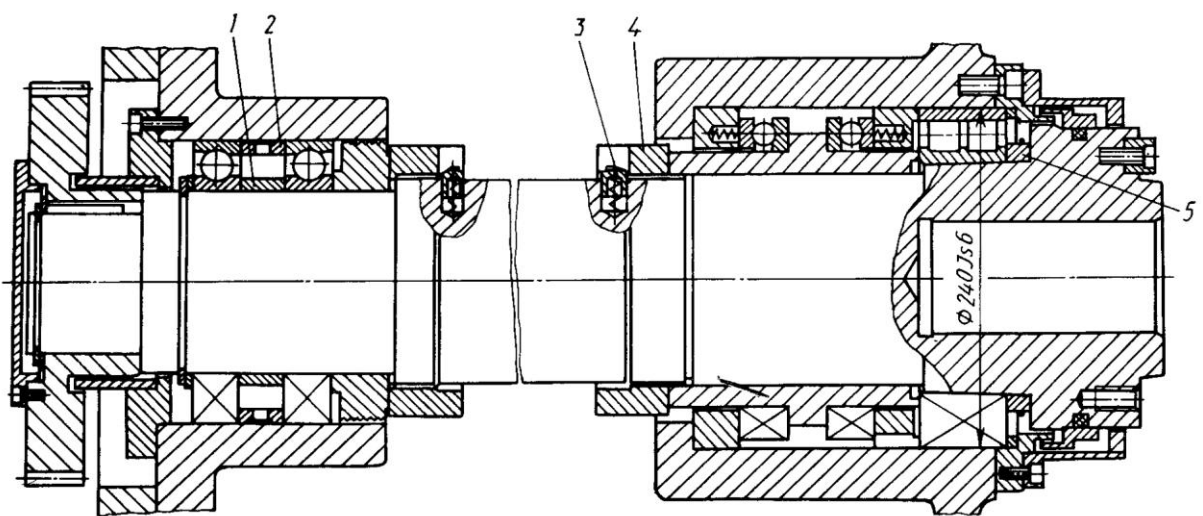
Шпиндельний вузол розточувальної бабки агрегатного верстата
